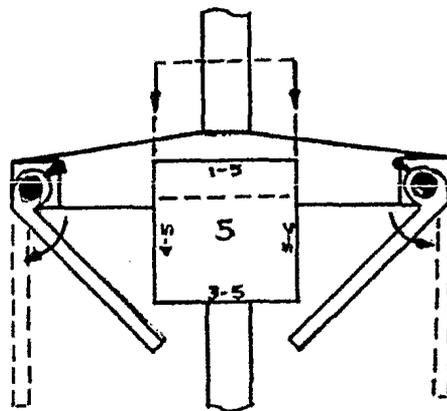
Accionamiento de las platinas para caída del embalaje.
